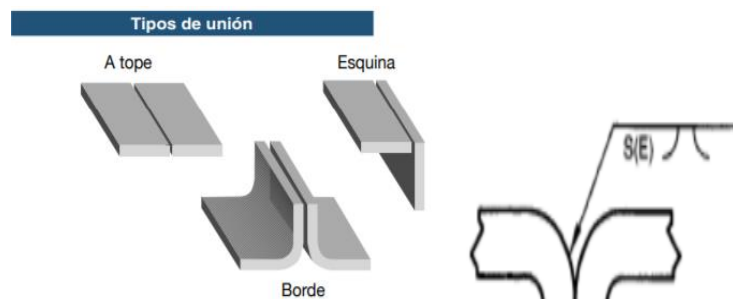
Tipos de juntas de soldadura [27].
